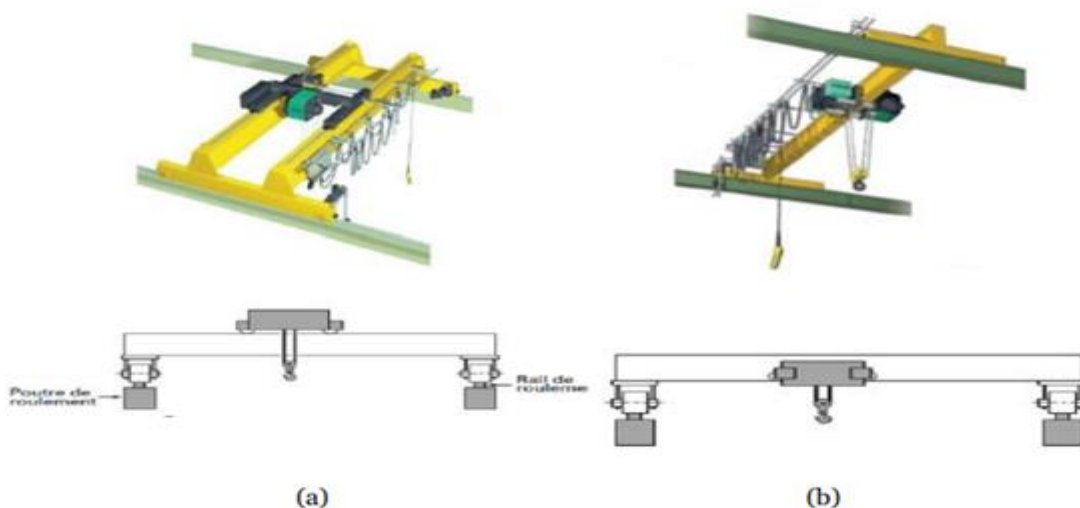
(a) pont roulant bipoutres pose, (b) pont roulant mono poutre pose
